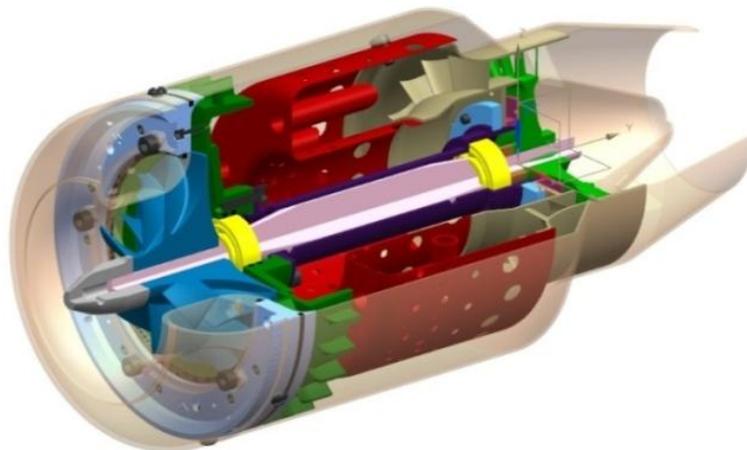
3D модель малоразмерного воздушно-реактивного двигателя типовой схемы.
